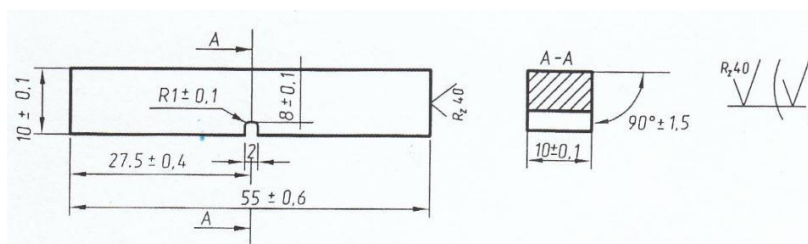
Образец для испытаний на ударный изгиб
